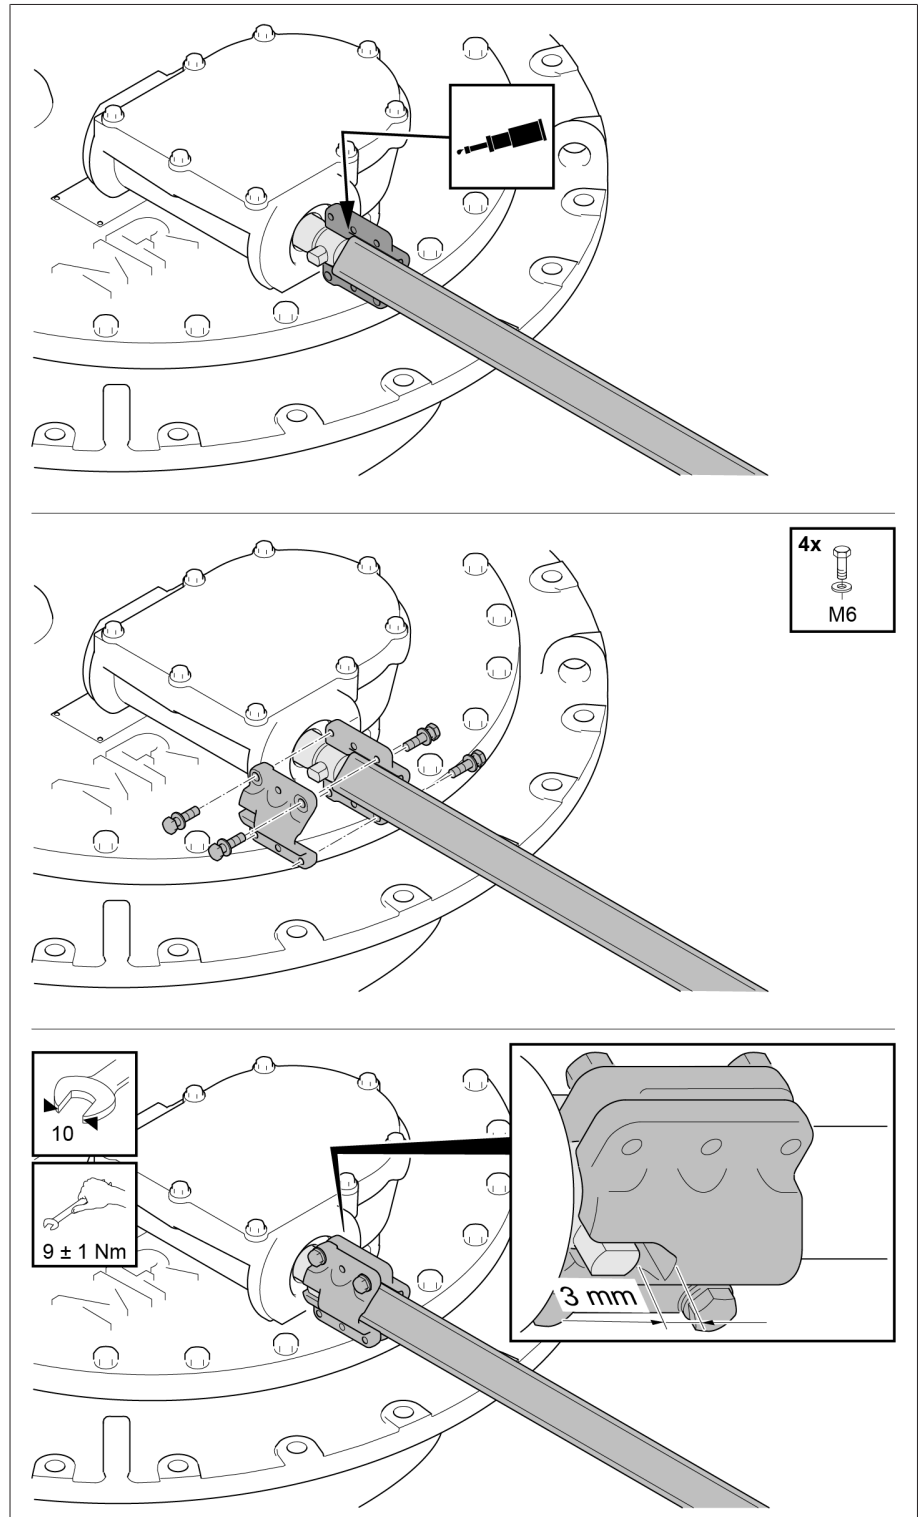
Fijación del tubo cuadrado en el engranaje reductor superior
